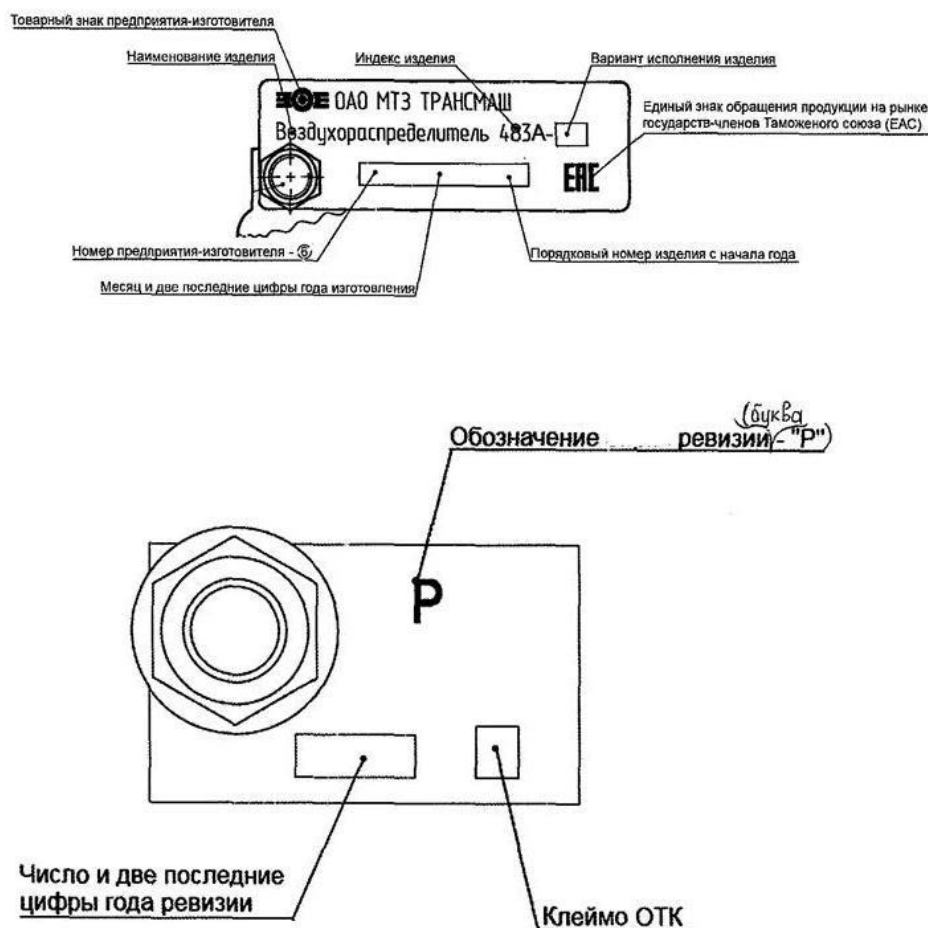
Расположение маркировки на бирке заводской после изготовления и ревизии воздухораспределителя
